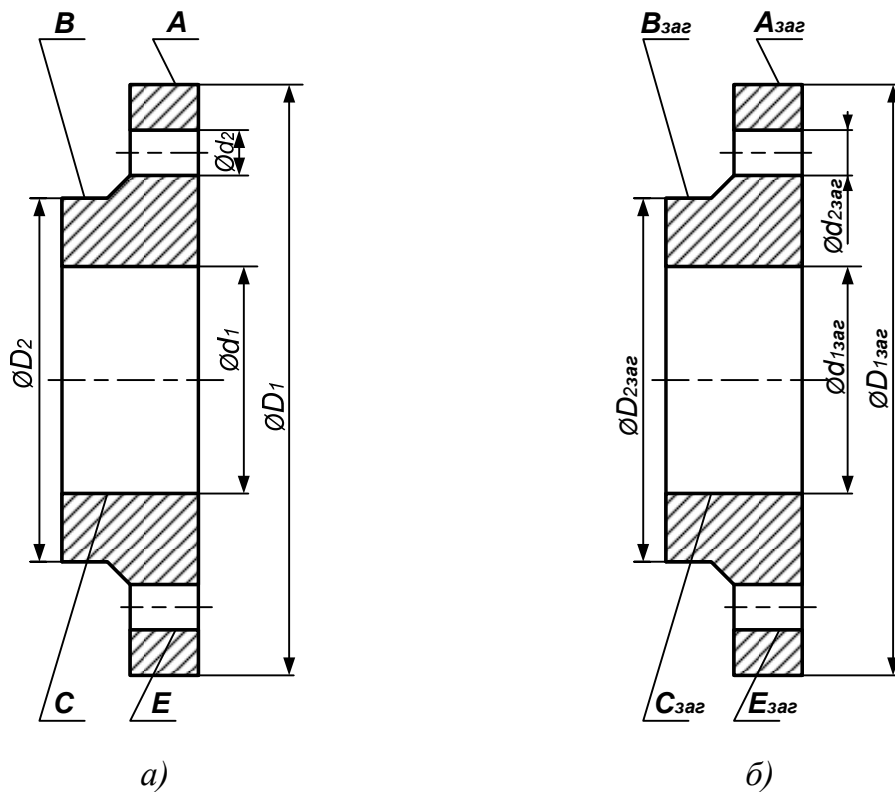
Эскизы фланца (а) и заготовки (б)
